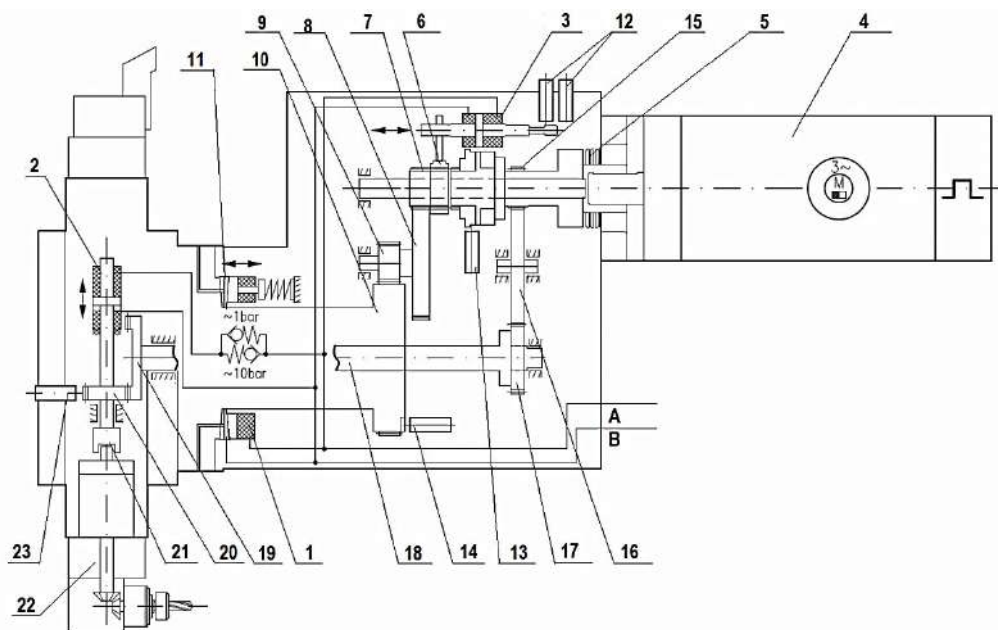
Схема револьверної головки Sauter мод. 0.5.450
